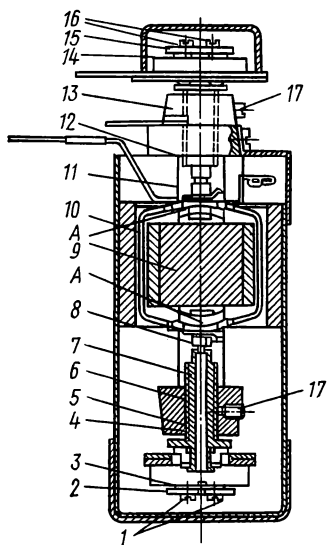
Обойма для сборки измерительного механизма с подвижной частью на растяжках:
